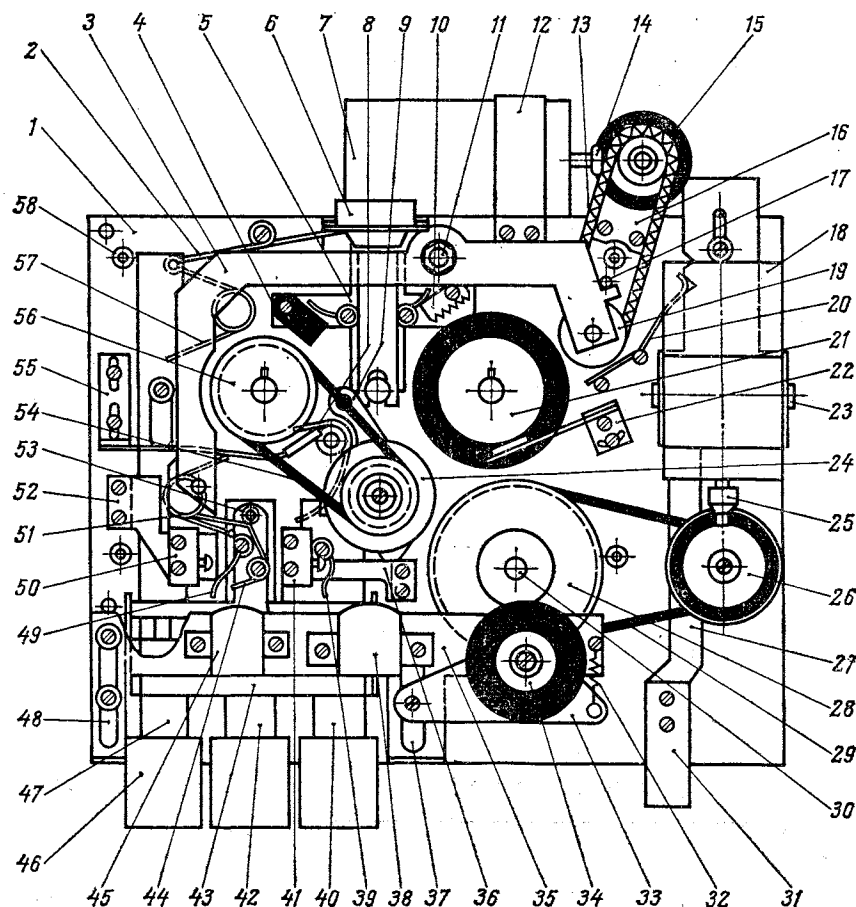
Лентопротяжный механизм в сборе: 1 — панель лентопротяжного механизма, Д16Д-Т, лист толщиной 2,5 мм; 2 — рычаг тормоза; 3 — рычаг ролика приемного узла; 4 — колодка тормоза подающего узла; 5 — планка тормоза; 6 — кнопка выталкивателя кассеты; 7 — электродвигатель приемного узла (М2); 8 — пружина кнопки «<»; 9 — рычаг промежуточного ролика; 10 — колодка тормоза приемного узла; 11 — стойка; 12 — скоба, Л62-Т; 13 — пружинный пассив, проволока стальная; 14 — насадка, Ст. 2Х13; 15 — обрезиненный ролик; 16 — планка; 17 — упор; 18 — ведущий электродвигатель (М1); 19 — шкив; 20 — фиксатор, проволока стальная класса II диаметром 0,6 мм; 21 — подкатушечник приемного узла; 22, 55 — подтормаживающие устройства; 23 — полуось, ЛС59-1; 24 — промежуточный ролик; 25 — насадка, Ст. 2Х13; 26 — промежуточный шкив ведущего узла; 27 — каретка, Л62-Т; 28 —
